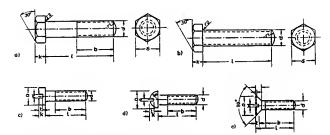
a) Sechskantschraube nach DIN 931; b) Sechskantschraube nach DIN 933; c) Zylinderschraube nach DIN 84; d) Halbrundschraube nach DIN 86; Senkschraube nach DIN 87
